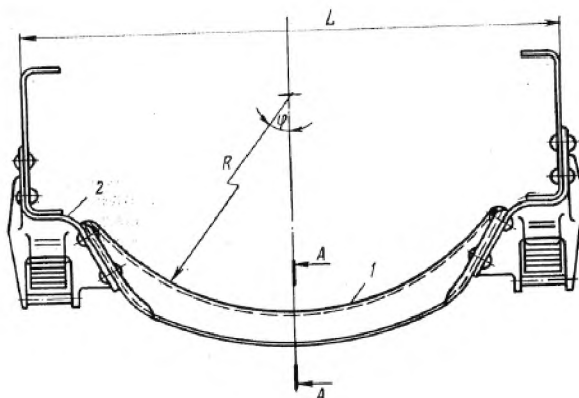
Вид рамы коробчато-балочного типа по фронту
